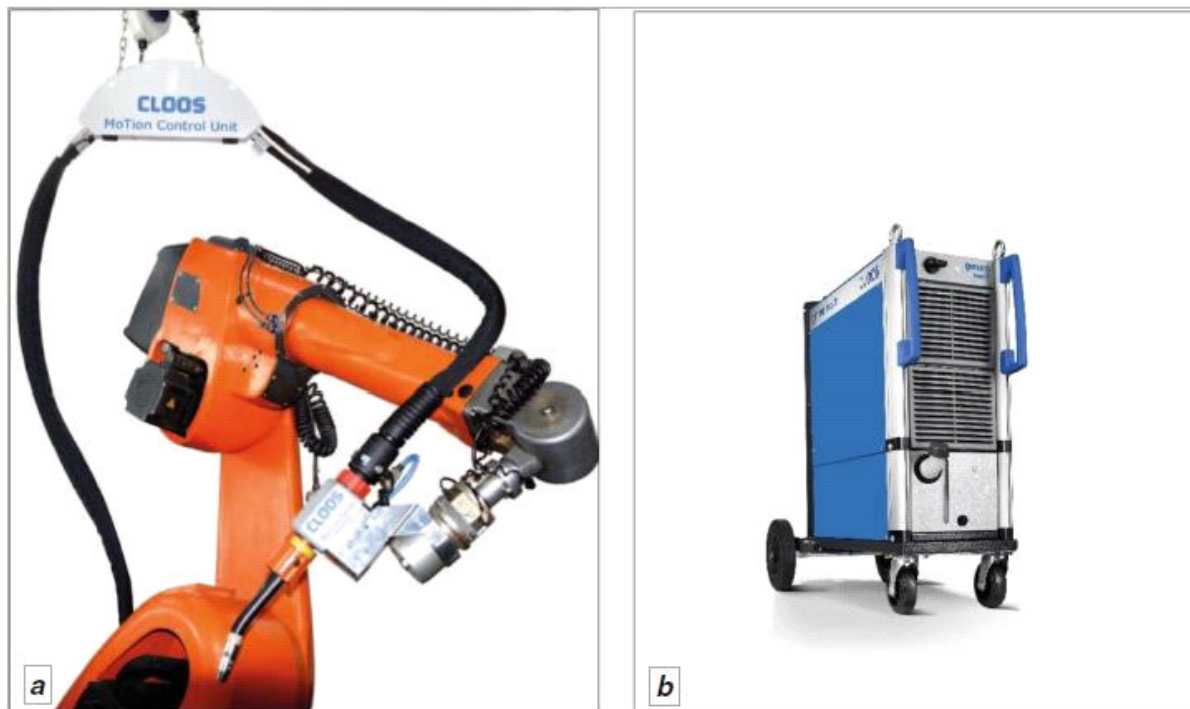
Hauptkomponenten des Schweißsystems mit bidirektionaler Drahtbewegung: "MoTion Control Unit" und "Motion Drive" (a) Schweißstromquelle "Qineo NexT" (b)
